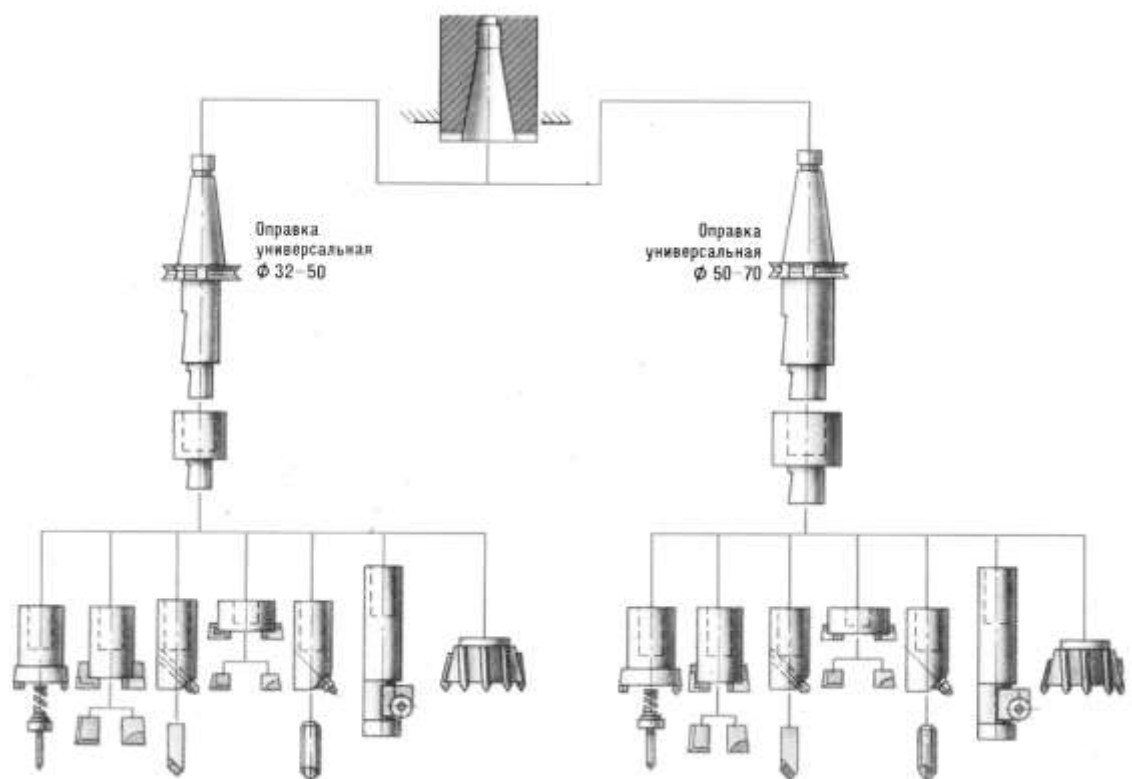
Модульна система інструменту для свердлильно-фрезерно-розточувальних ГПМ
